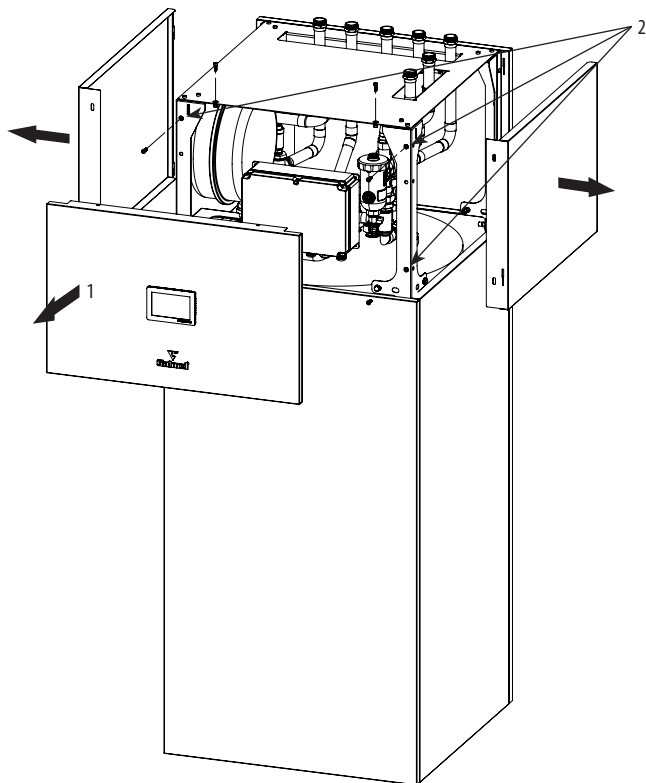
Onebox - Entfernung der Seitenwände des Gehäuses
